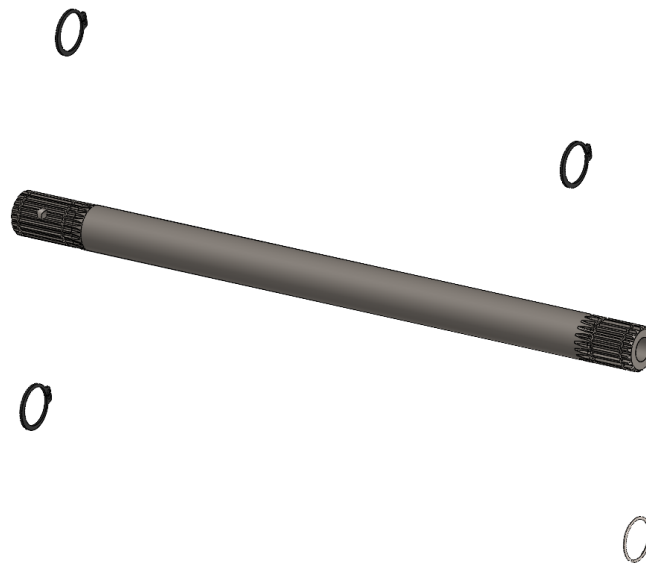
Explosionado subensamblaje del palier. Elaboración propia.
